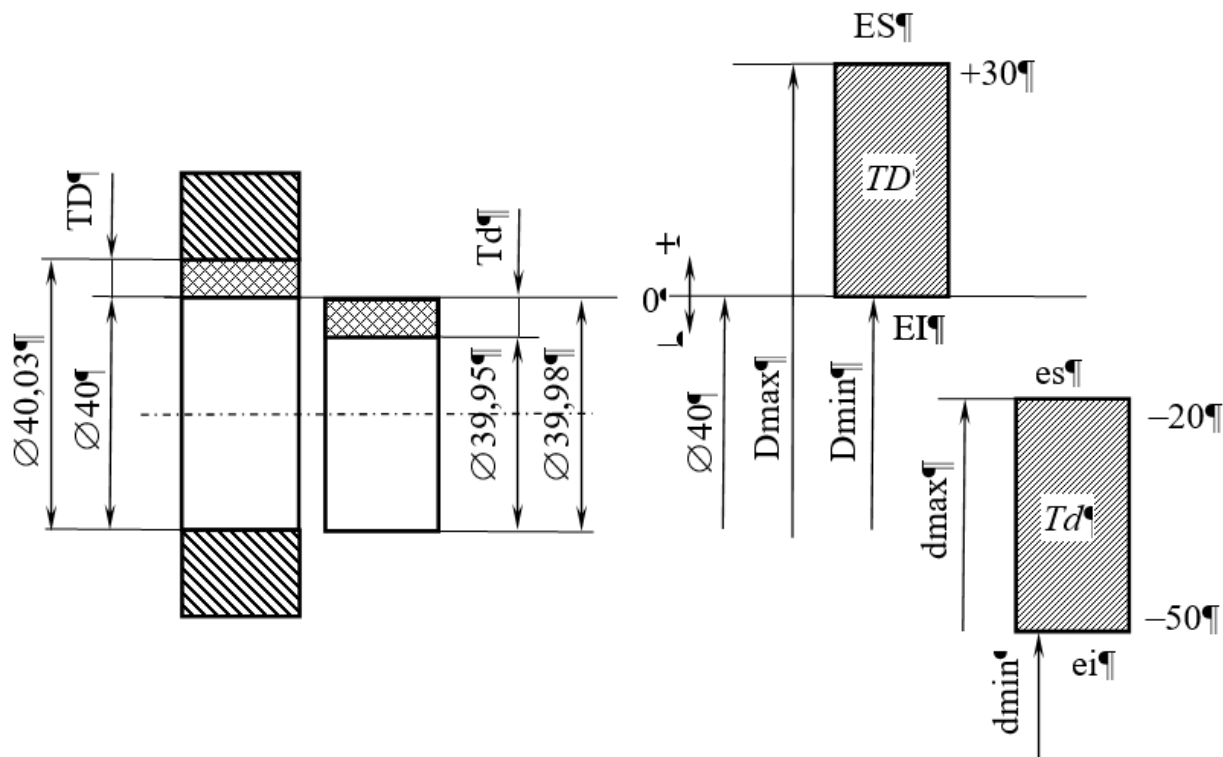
Схема розташування полів допусків.
